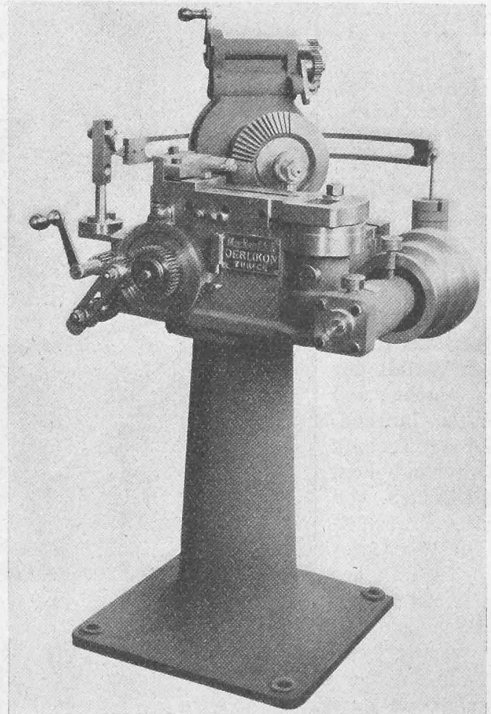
Räderhobelmaschine für Kegelräder bis 200 mm Durchmesser.
